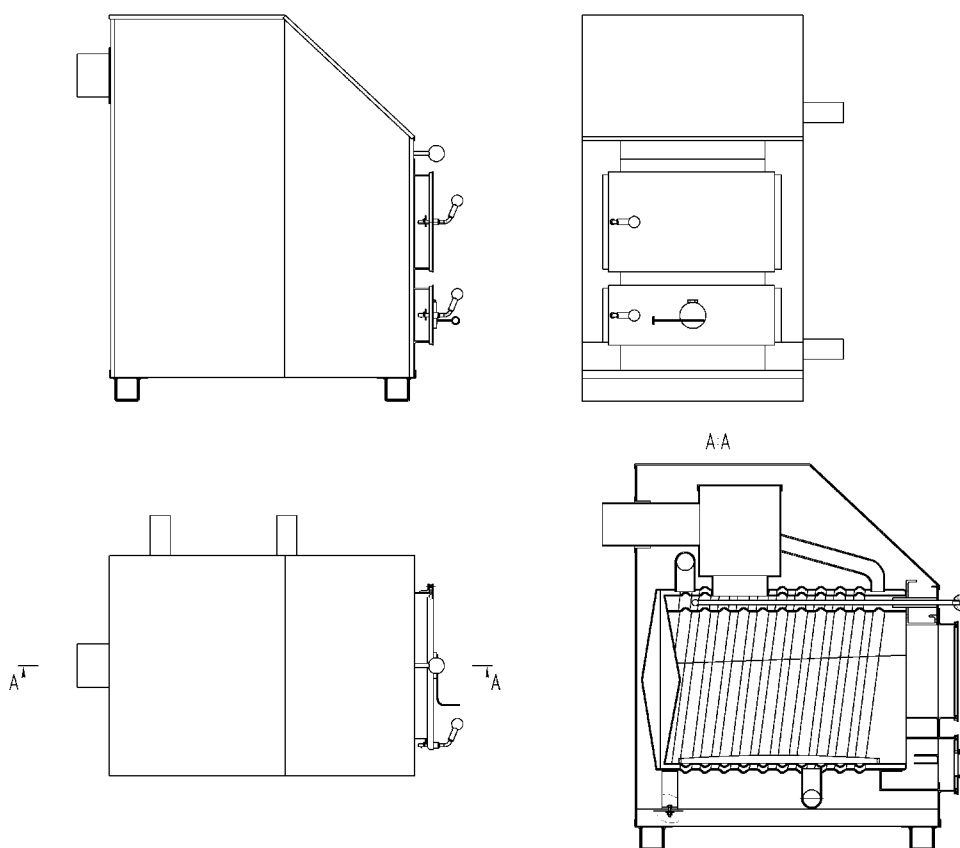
Конструкция газогенераторного котла КМВ 2-20-0,125
